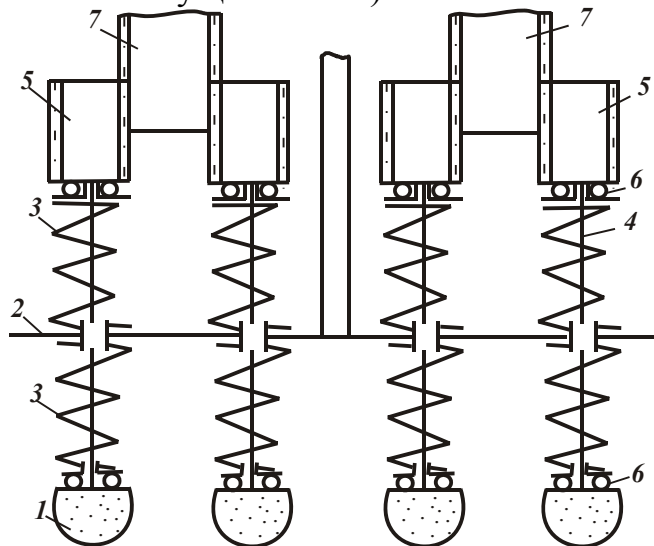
Шлифовальный инструмент для обработки фасонных поверхностей: 1 - шлифовальный шар; 2 - несущая плита - корпус; 3 - пружины; 4 - жесткий вал; 5 - подвижные шестерни-валы; 6 - подшипники; 7 - приводные шестеренчатые валы.
